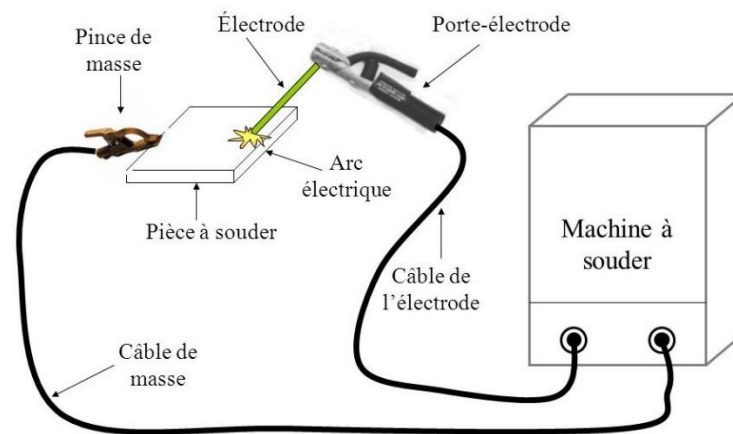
Principe du soudage à l'électrode enrobée
